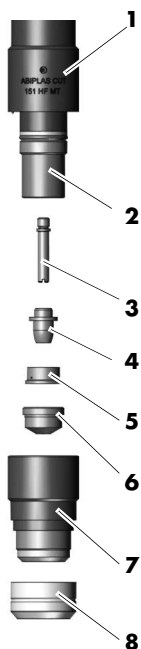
Vue d'ensemble d'ABIPLAS® CUT 111 HF MT
